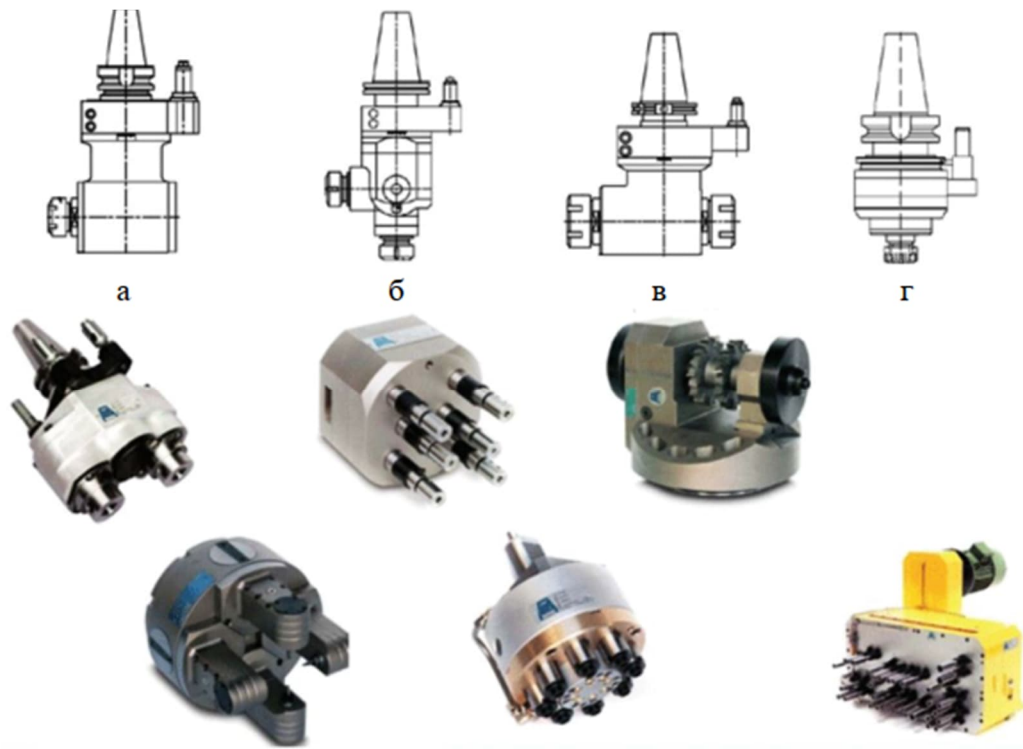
Приводний інструмент для верстатів фрезерної групи з ЧПК: державний цанговий держак (а); поворотний цанговий держак (б); радіальний цанговий мультиплікаторний держак (в); прискорювальна головка (г)
